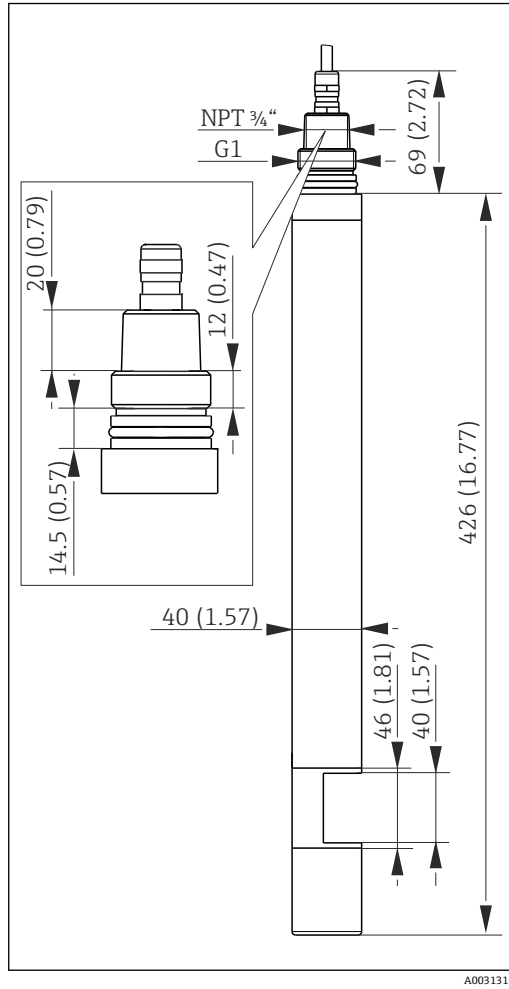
传感器 (40 mm 光程) 的外形尺寸示意图;
